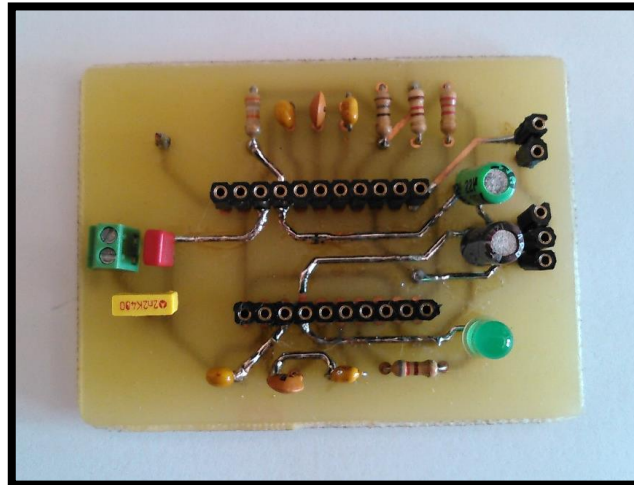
PCB del circuito del chip bq51050B final (TOP)
